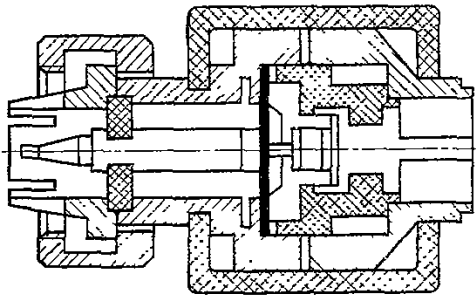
Конструкция болометрического преобразователя М5-46
